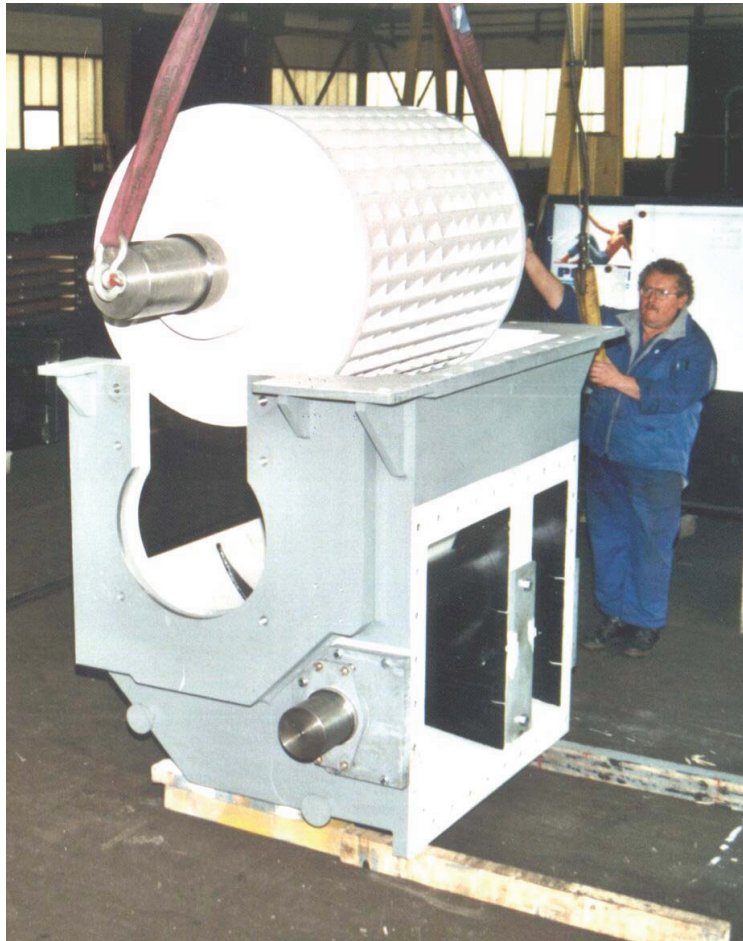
Montage des Lauftrades in radialer Richtung zur Turbinenachse
